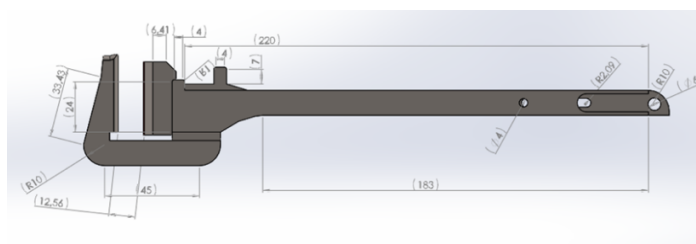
Корпус з опорною частиною та штовхачем в складі
